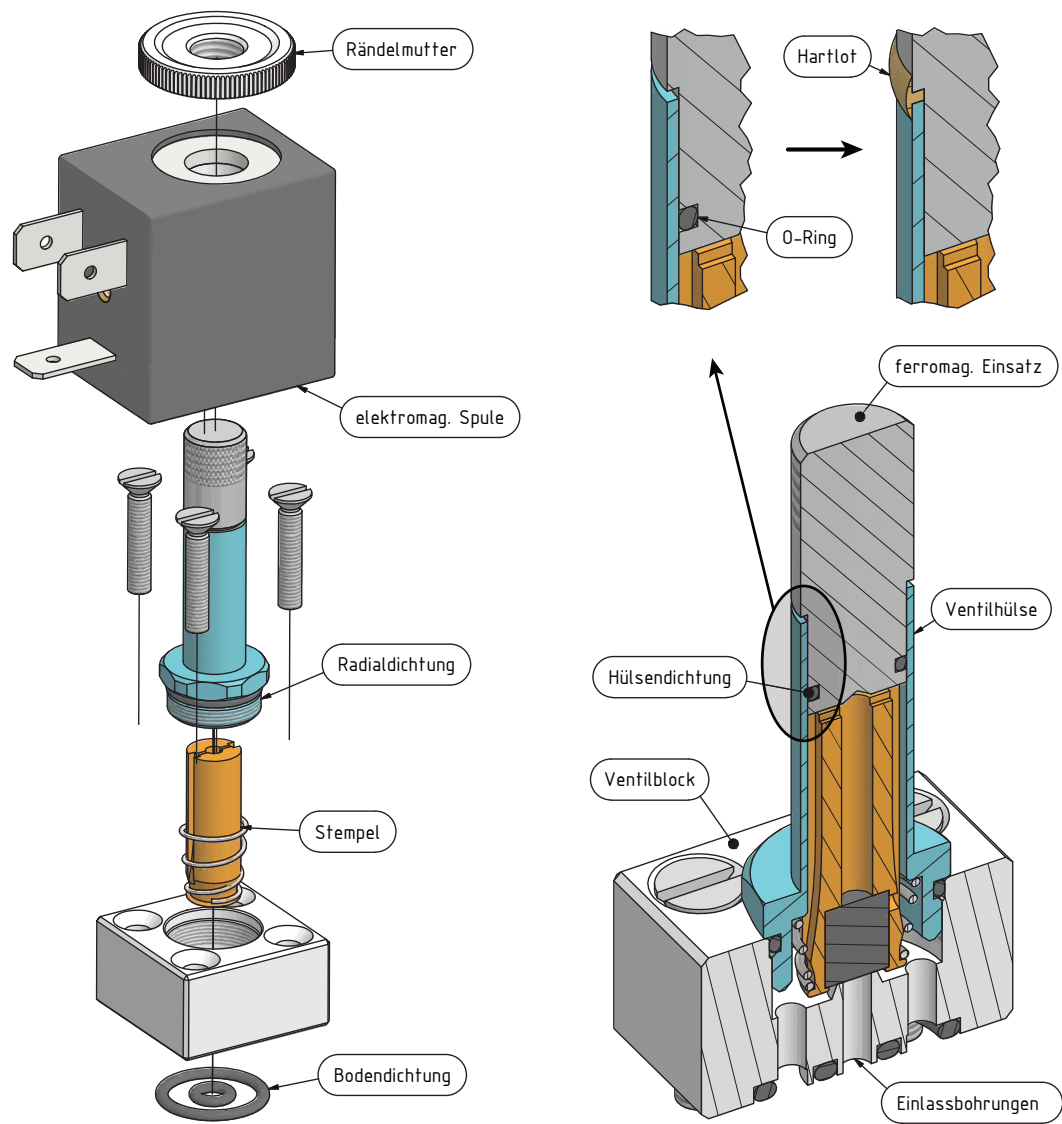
Explosions- und Schnittansicht eines IGH-Ventils
